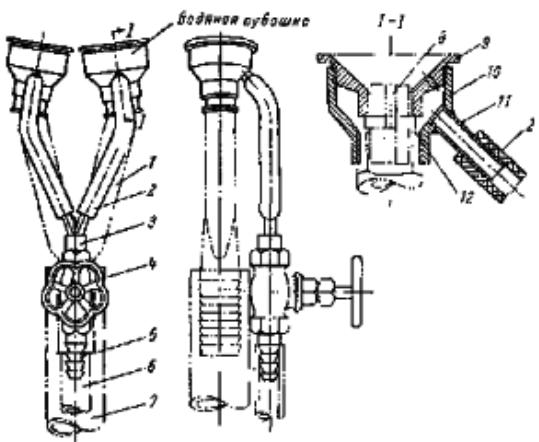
Приспособление для гидропескоструйной очистки фасадов
